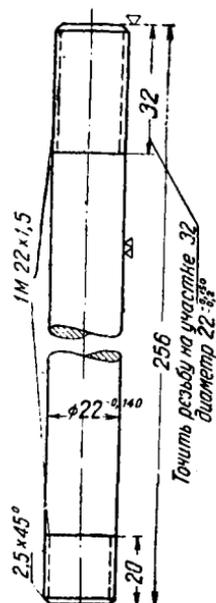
Дет. 1920. Шпилька втулки ведущего колеса
